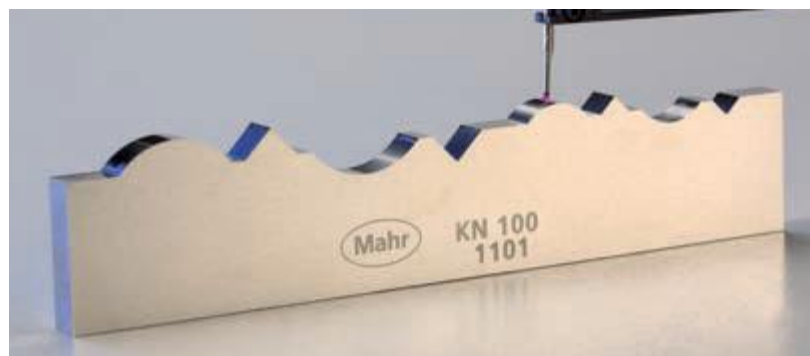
Общий вид мер для поверки приборов для измерений контура поверхности KN 100
